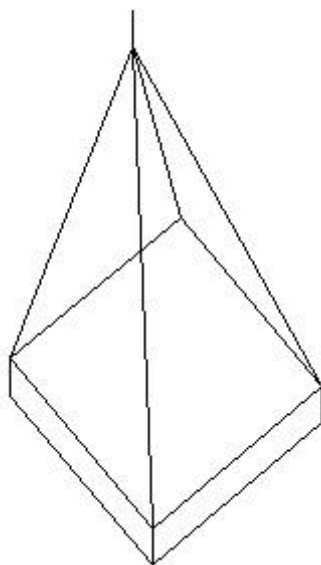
Mehanizam za prihvat boca pričvršćen za plafon
